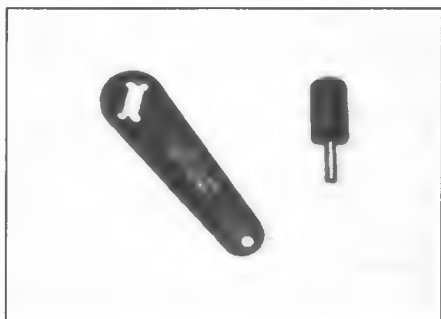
,а. Специальное приспособление компании Land Rover для выверки положения реле блокировки стартера
